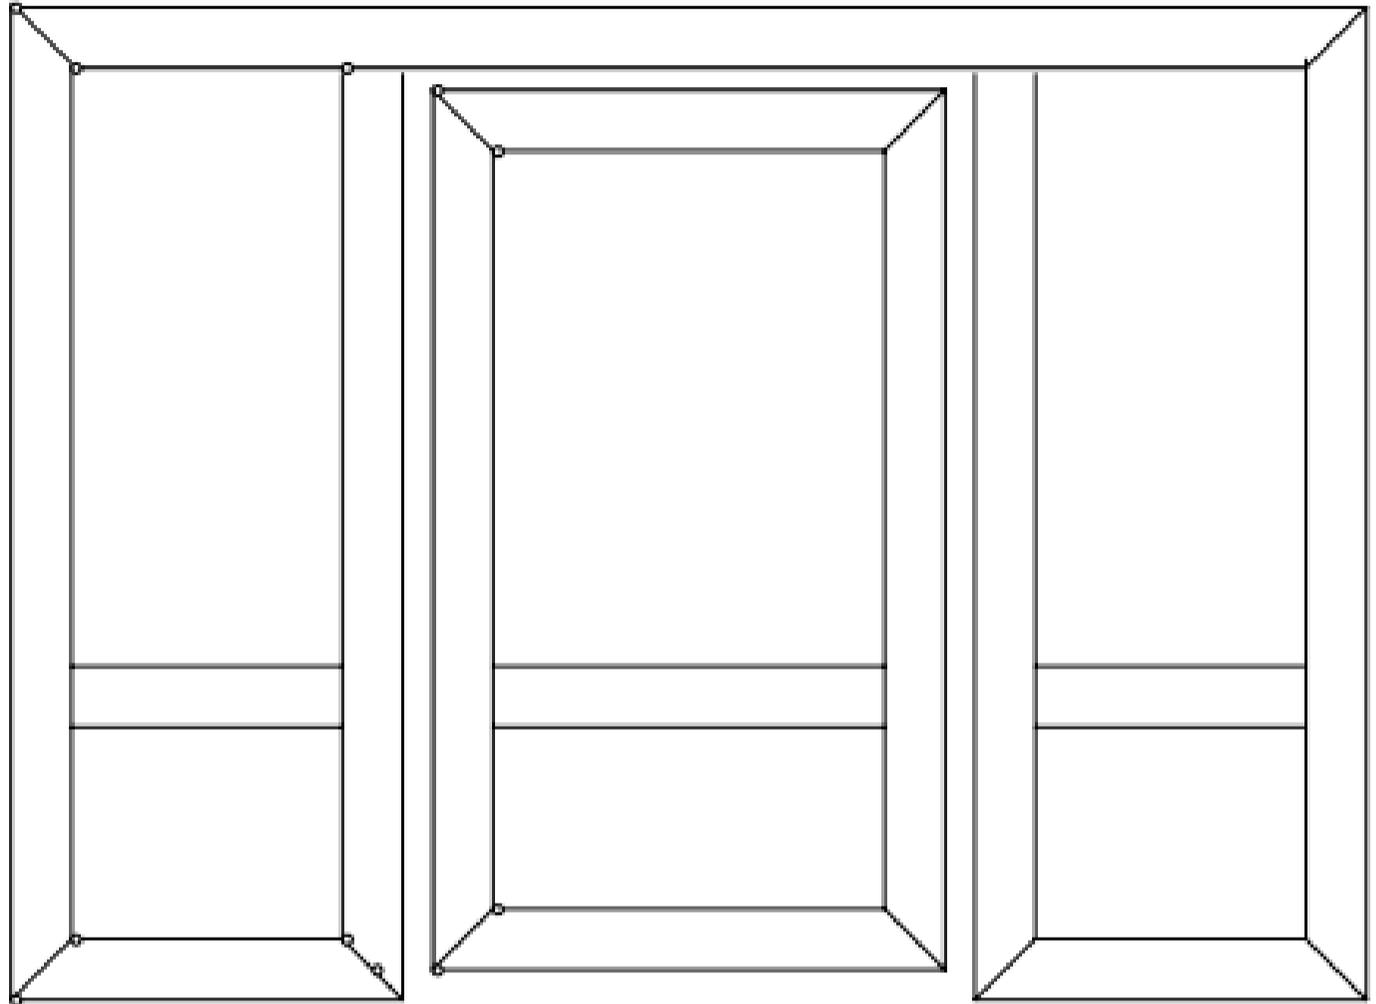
Tubos cuadrados después de colocarse los puntos de soldadura
